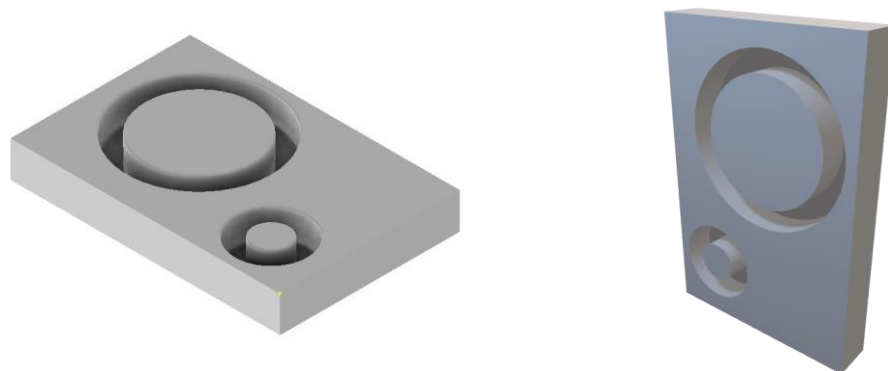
Τρισδιάστατη απεικόνιση αποστολής 46
